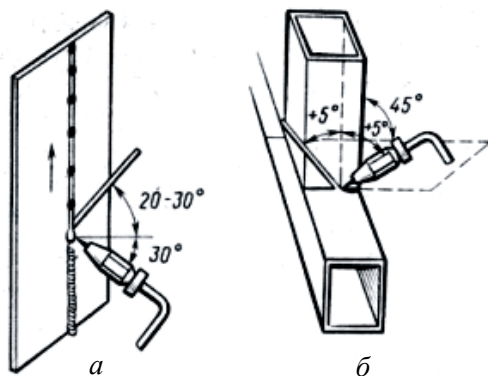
Последовательность наложения сварочного шва:
